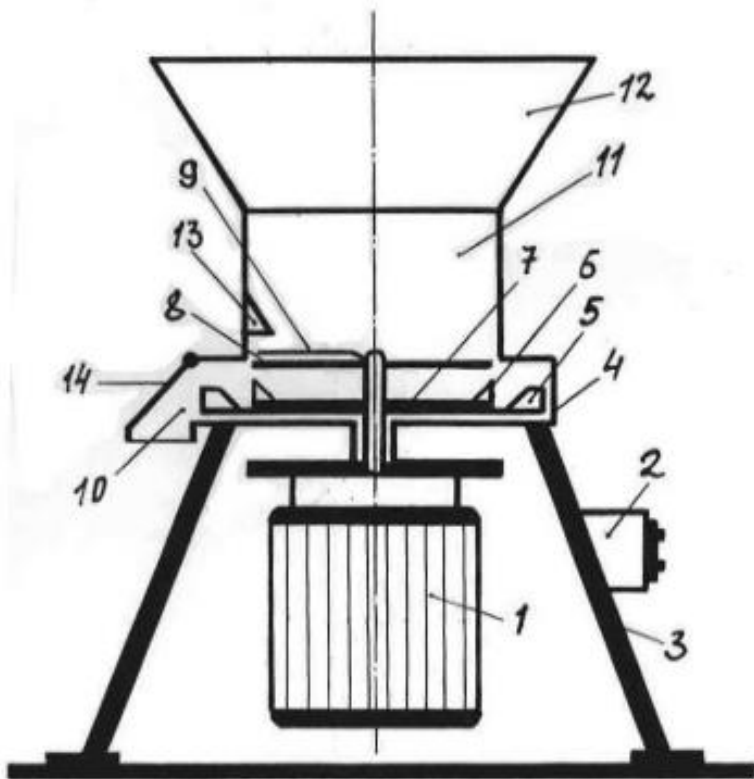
Технологічна сема корнерізки КПІ-4:1 - електродвигун; 2 - магнітний пускач; 3 - станина; 4 - корпус подрібнювача; 5 - лопать; 6 - вертикальний ніж; 7 - нижній диск; 8 - верхній диск; 9 - горизонтальний ніж; 10 - вивантажувальна горловина; 11 - бункер; 12 - завантажувальна горловина; 13 - протирижуча пластина; 14 - козирок.
